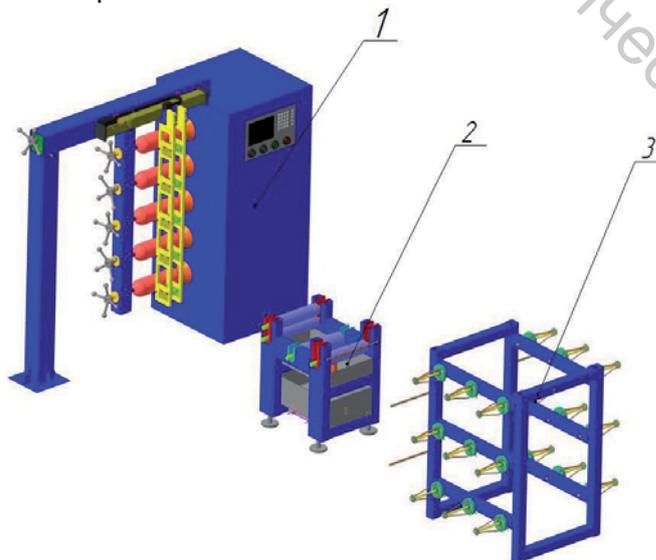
Общий вид автоматической установки для формования сосудов высокого давления из стеклокомпозита:
